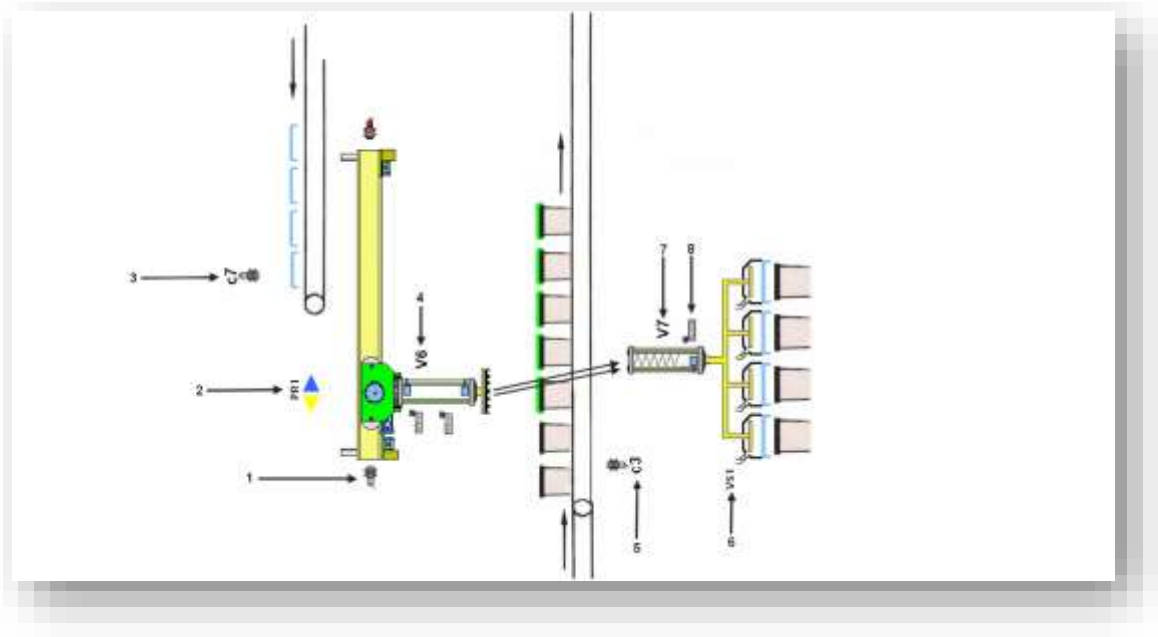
Etape de soudage de couverture de l'aluminium.
